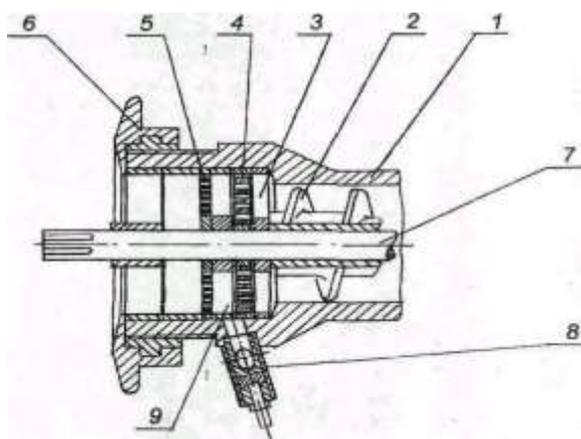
Камера ножевая с жировочным устройством: 1 – корпус рабочей камеры; 2 – шнек подающий; 3 – ножи; 4 – решетка входная; 5 – решетка выходная; 6 – гайка; 7 – вал; 8 – устройство жировочное; 9 – нож жировочный
